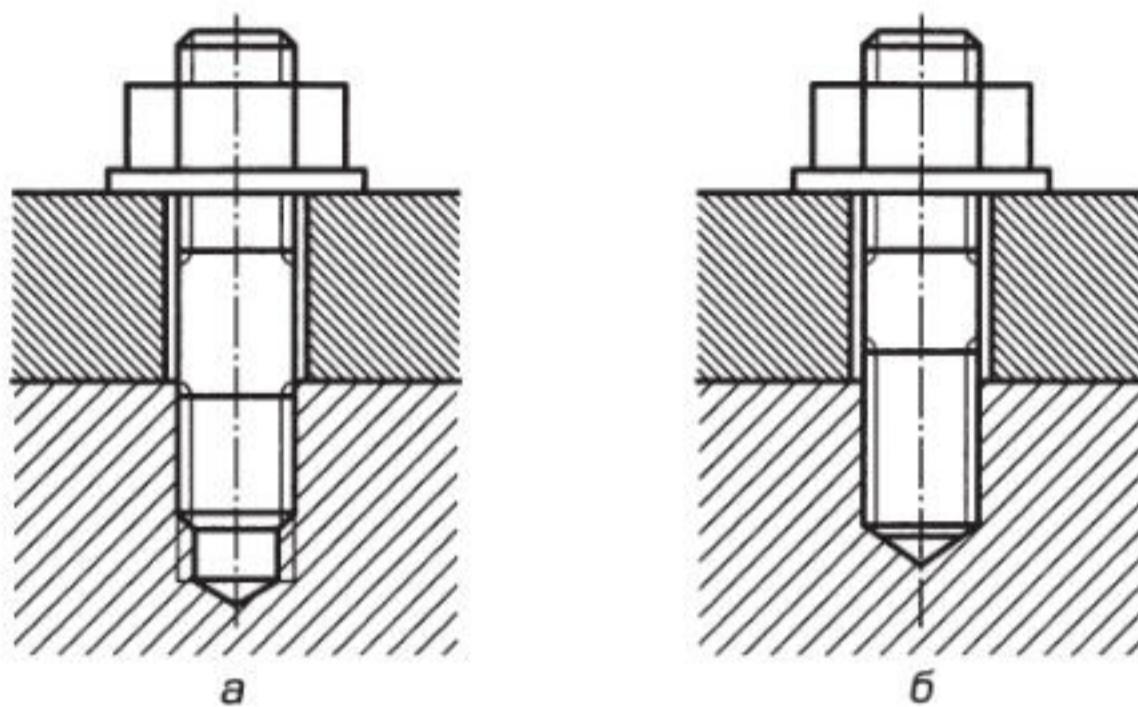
Соединение шпильками с заклиниванием на сбеге резьбы шпильки (а) и резьбового гнезда (б)
